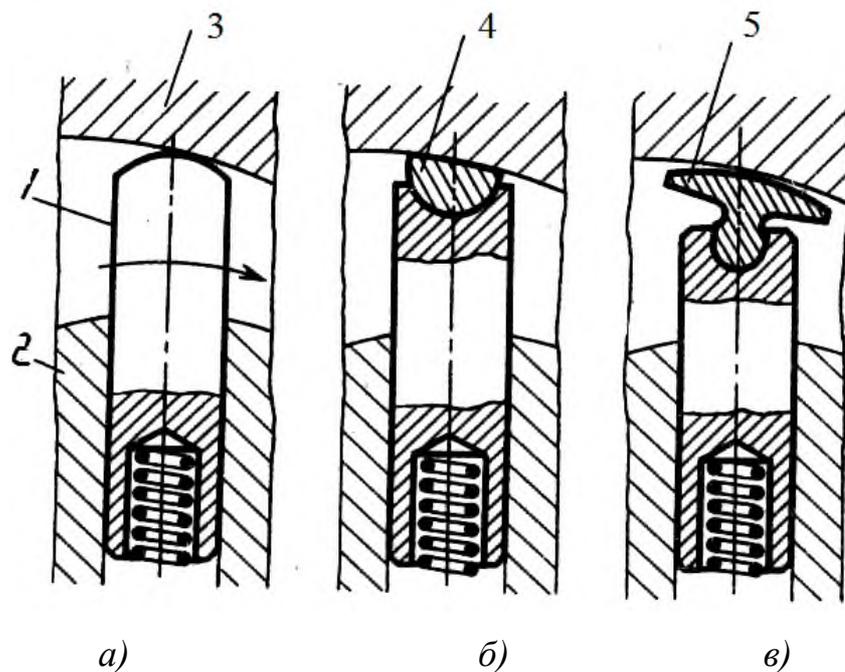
Замена линейного контакта лопатки 1 с корпусом 3 лопастного насоса поверхностным контактом, путём установки шарнирного вкладыша 4 или самоустанавливающегося башмаком 5
